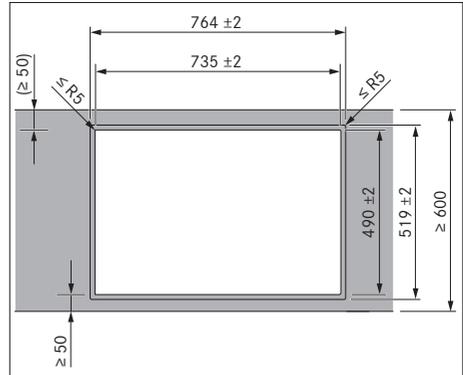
Dimensioni del taglio per montaggio a filo
